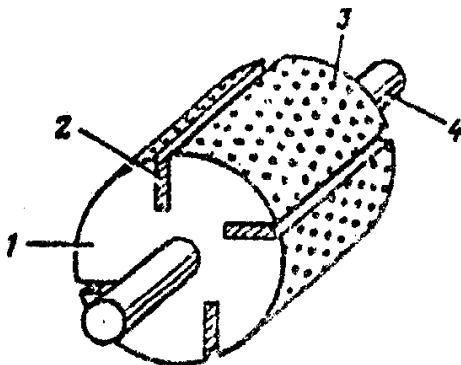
Ротор вакуум-насоса (крупорушки): 1 - ротор; 2 - пазы со стальными пластинками; 3 - насечка на роторе; 4 - ось ротора
